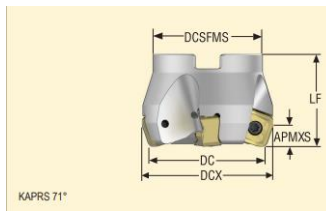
Торцева фреза R220.56-0125-14-12A [7, с.122]
